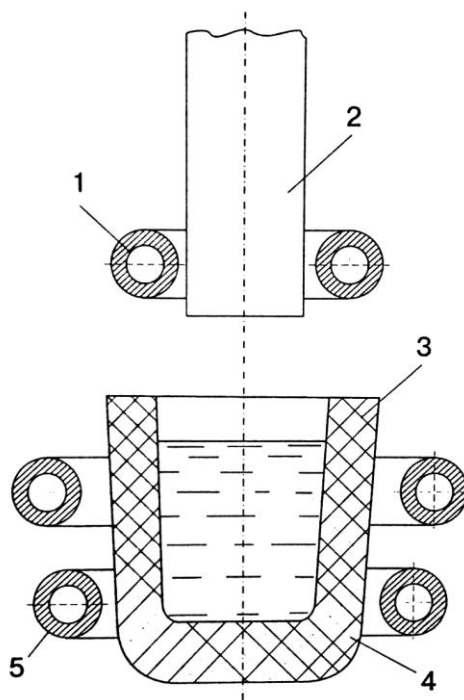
Наплавка погружением подогретой детали в форму-тигель с расплавленным металлом:
